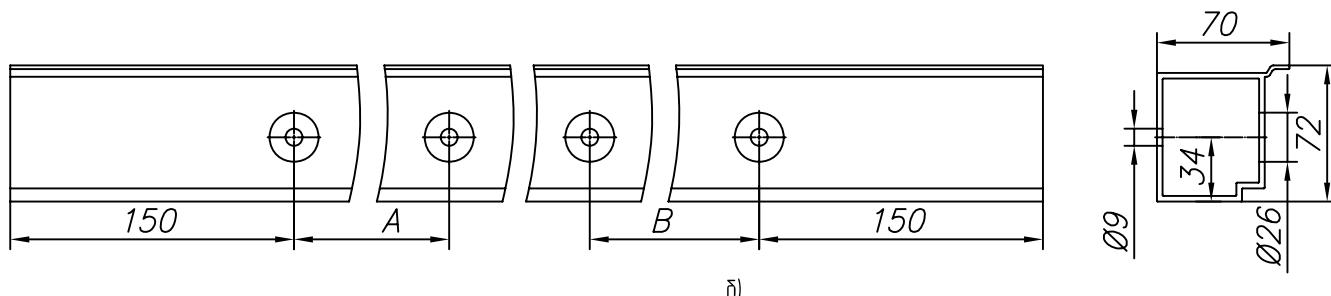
Изготовление соединителя углового FLGU.400.0914
